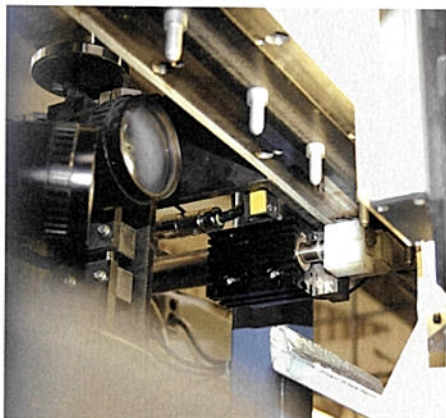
Produktausstoßer mit 580 Takte/min für die Gutteil-Ausbringung
